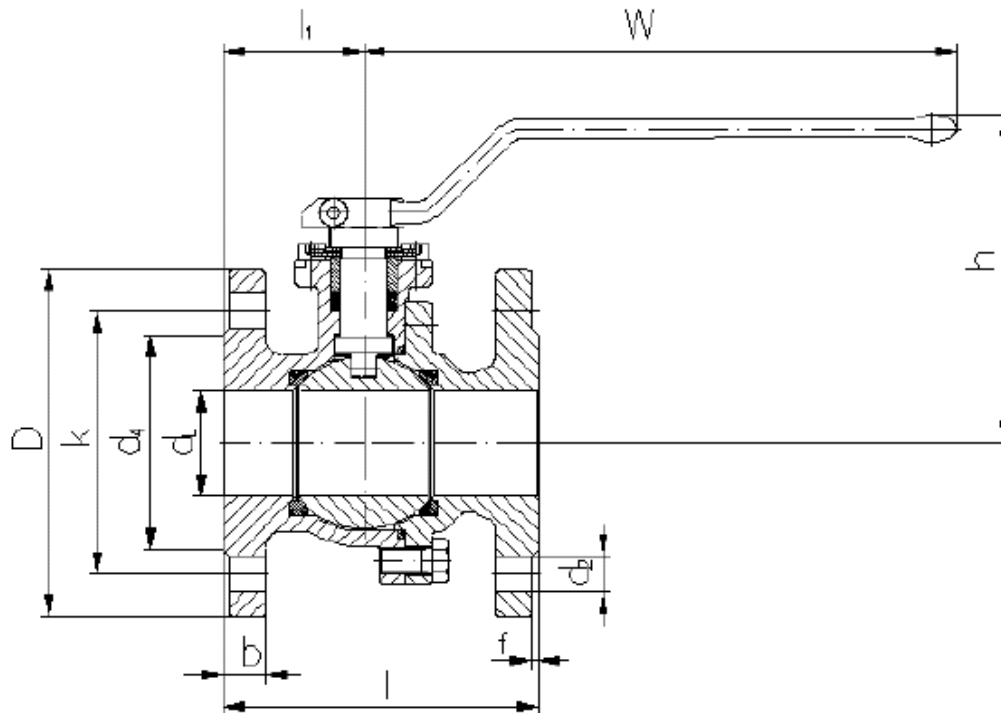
Kugelhahn mit Flanschanschluss nach DIN EN 1092-1 Form B1; Baulänge Grundreihe 27 (kurz) nach EN 558-1 (F18 nach DIN 3202 Teil 1)
